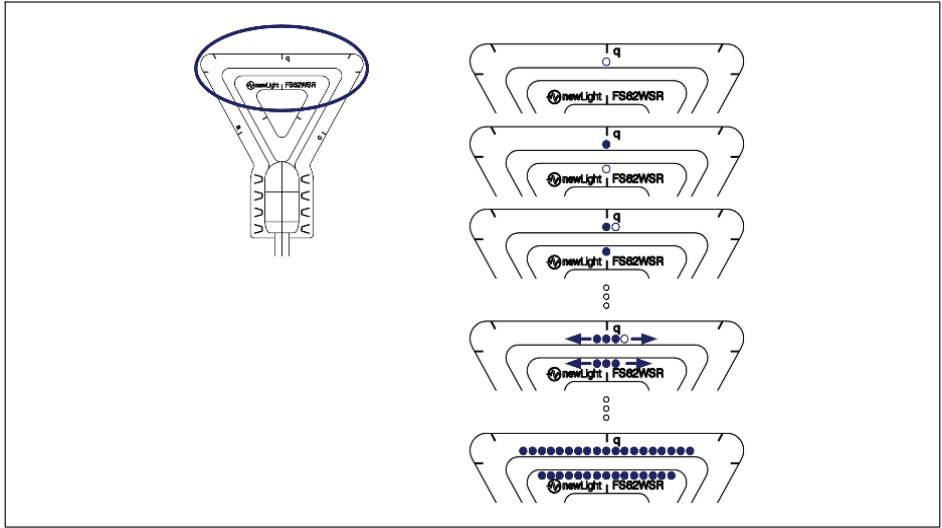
FS62WSR - parcours de soudage 1
